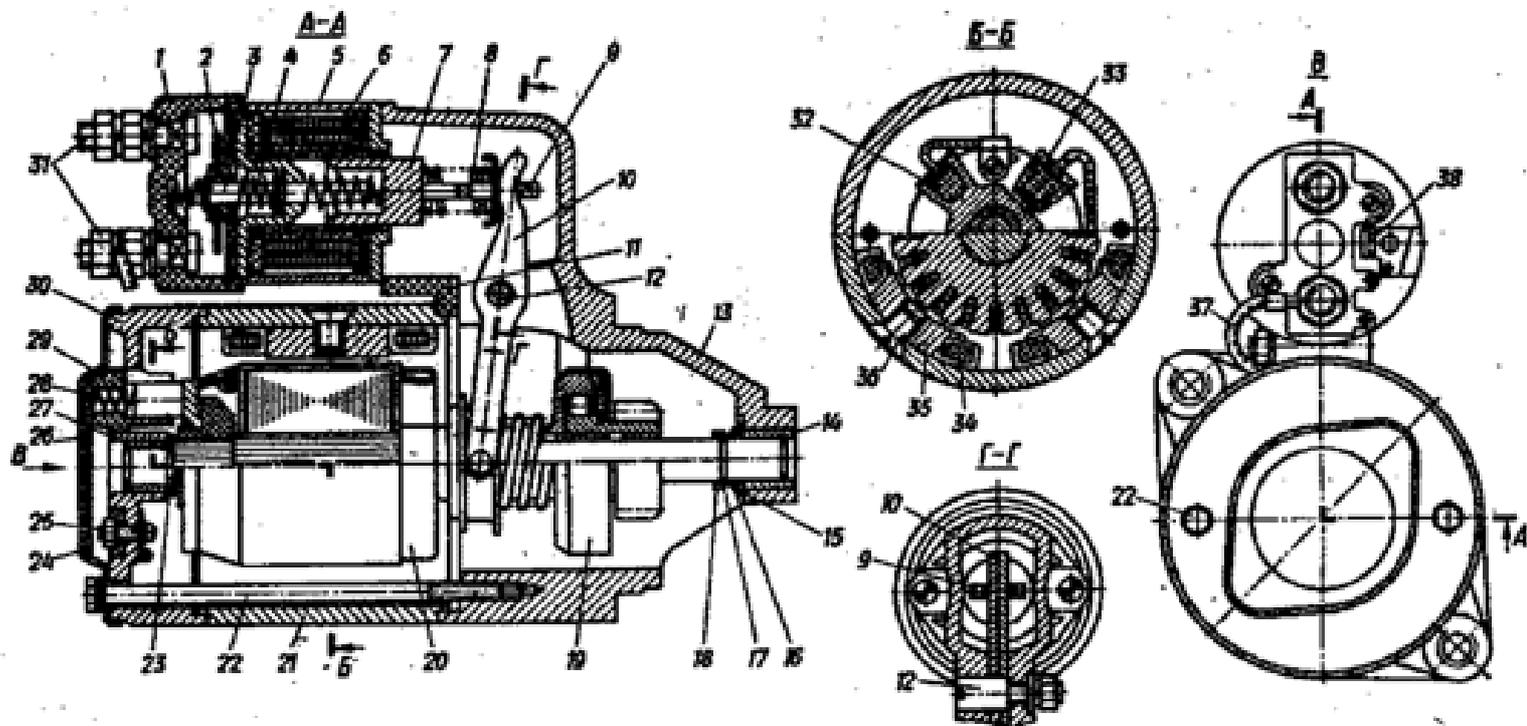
Стартер: 1 - крышка реле; 2 - контактный диск; 3 - шток реле в сборе; 4 - пружина контактного диска; 5 - корпус реле; 6 - обмотка реле; 7 - пружина якоря; 8 - якорь реле; 9 - серьга якоря; 10 - рычаг; 11 - прокладка; 12 - ось рычага; 13 - крышка со стороны привода; 14, 27 - втулки якоря; 15, 16, 23 - шайбы упорные; 17 - кольцо стопорное; 18 - кольцо упорное; 19 - роликовая муфта с шестерней; 20 - якорь в сборе; 21 - статор; 22 - стяжной болт; 24 - прокладка изоляционная; 25 - винт; 26 - колпак; 28 - пружина щетки; 29 - пластмассовый щеткодержатель; 30 - крышка со стороны коллектора; 31 - контактные болты тягового реле; 32 - щетка неизолированная; 33 - щетка изолированная; 34 - катушка возбуждения; 35 - полюс; 36 - полюсный винт; 37 - вывод от катушки возбуждения; 38 - вывод обмоток реле (штеккер внутренний)
